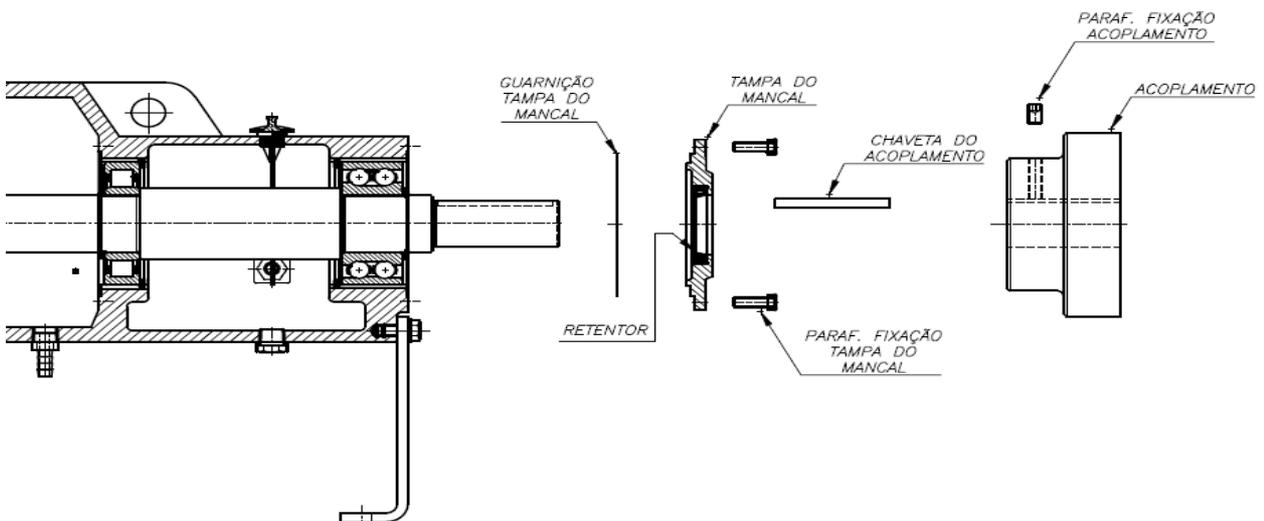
Removendo acoplamento e tampa traseira do mancal
